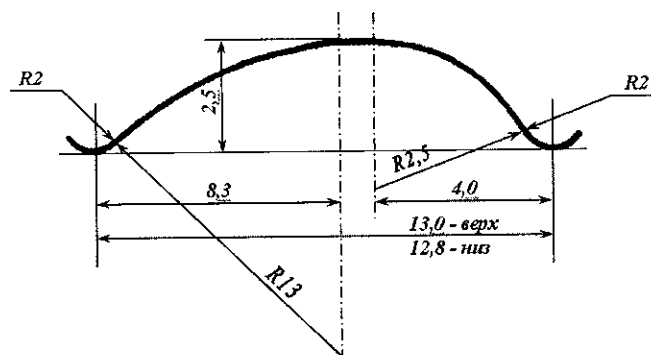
Профиль рифления кристаллизатора для отливки широких слябов
